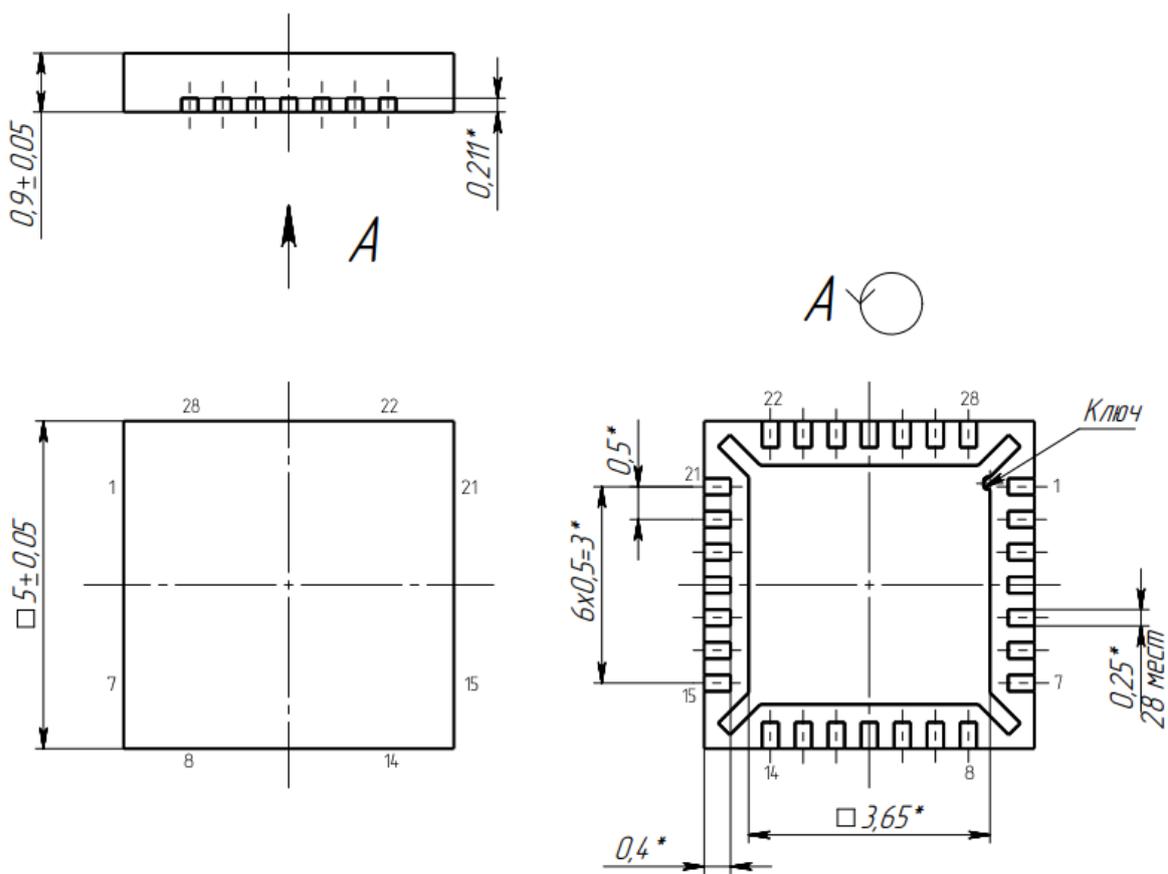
Габаритный чертеж корпуса 5102.28-1 К (размеры в мм)
